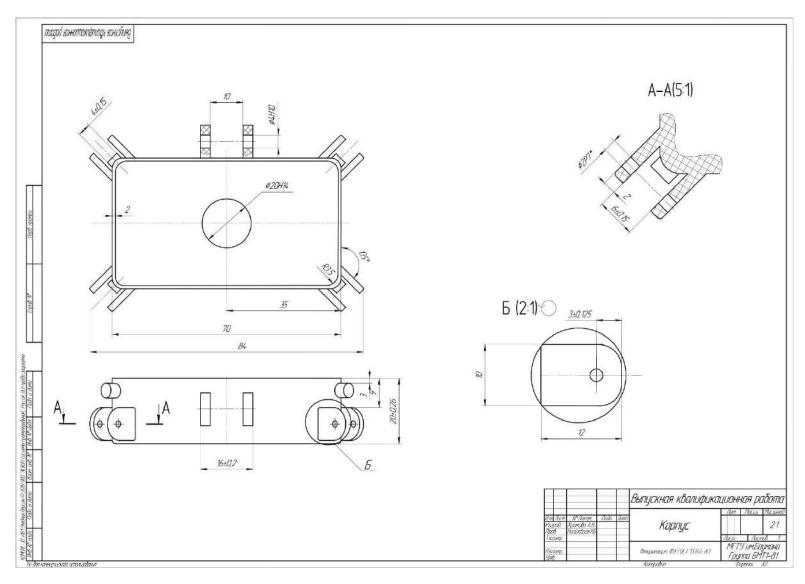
Чертеж детали (корпуса комбинированного датчика)
